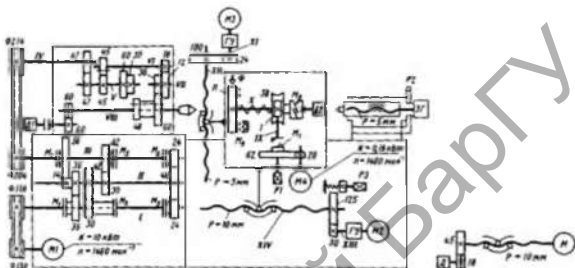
Кинематическая схема токарного станка 16К20Ф3 с ЧПУ
